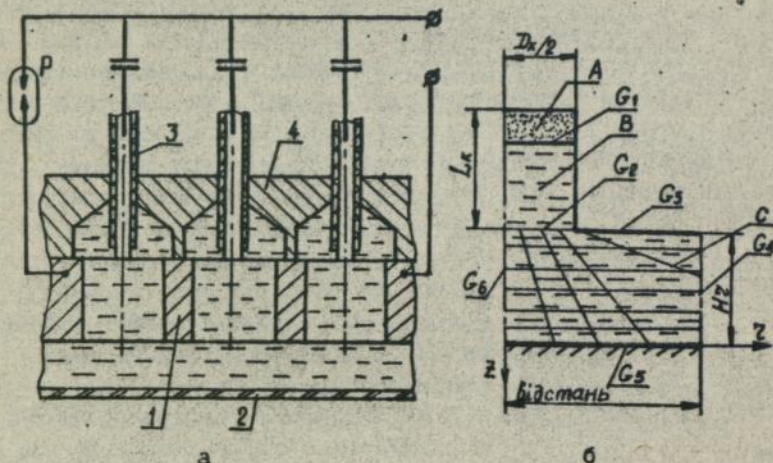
Принципова схема багатокамерного розрядного блока (а) та розрахункова схема зони течії (б): а: 1 - спрямовуюча плита; 2 - заготовочка; 3 - електрод; 4 - розрядна плита; P - формуючий розрядник; б: А, В, С - розрахункові ділянки; $G_1 - G_3$ - межі ділянок; тонкі лінії - структура розрахункової сітки.
